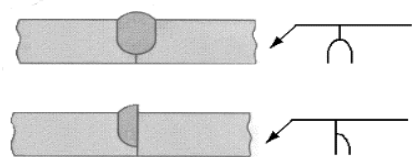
Soldaduras en U y J para placas gruesas.
